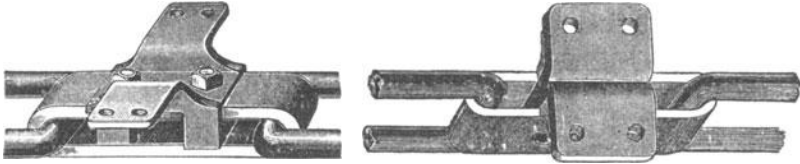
und 277. Befestigungsstücke für Flach-Rundeisenketten.
